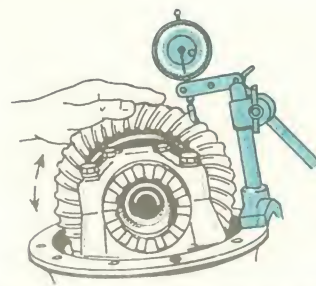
Проверка бокового зазора в зацеплении шестерен главной передачи при помощи индикатора.
